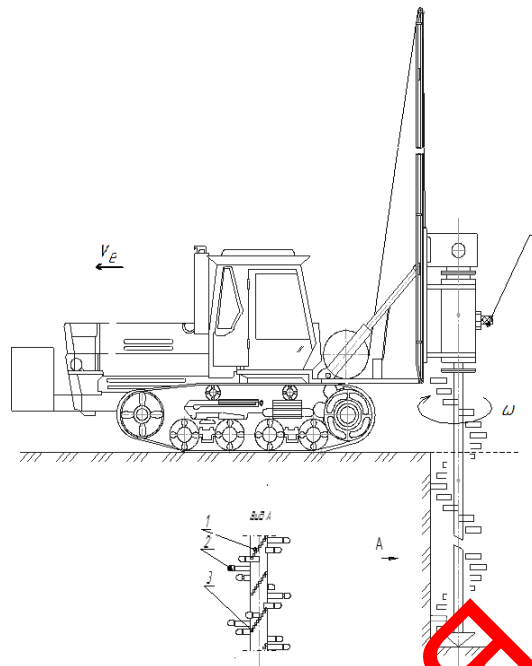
Робочий орган землерийної машини для видобування корисних копалин: 1 – пустотілий вал; 2 – різці; 3 – отвори, рознесені по висоті; 4 – водопровідний рукав [27].
